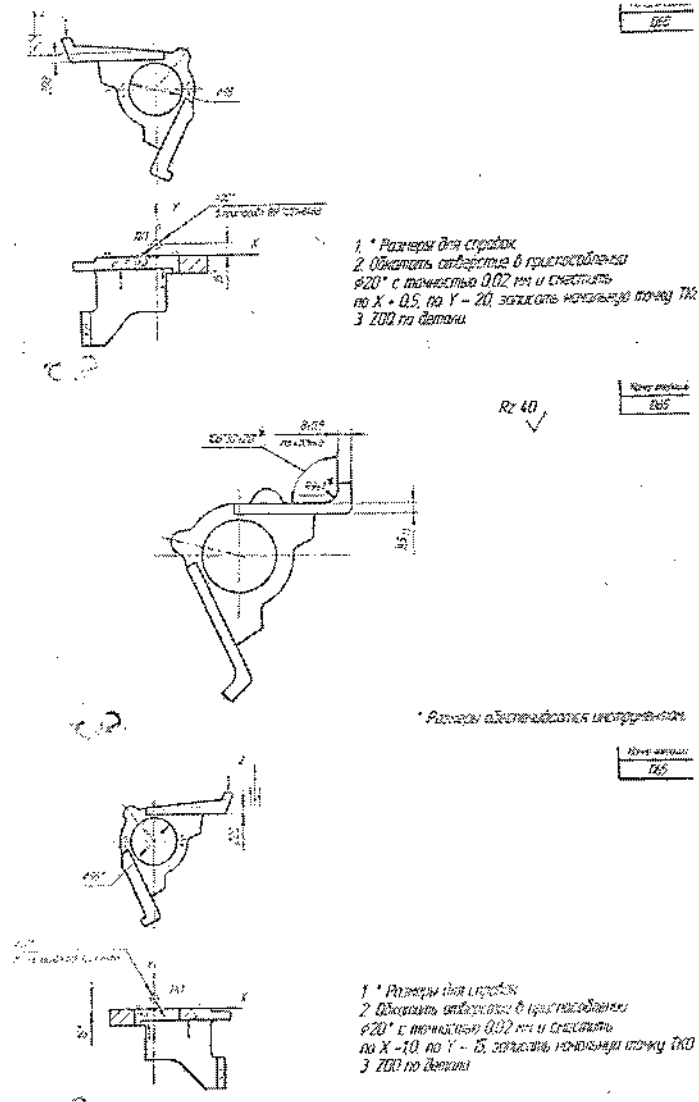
Эскизы на фрезерные операции с ЧПУ
